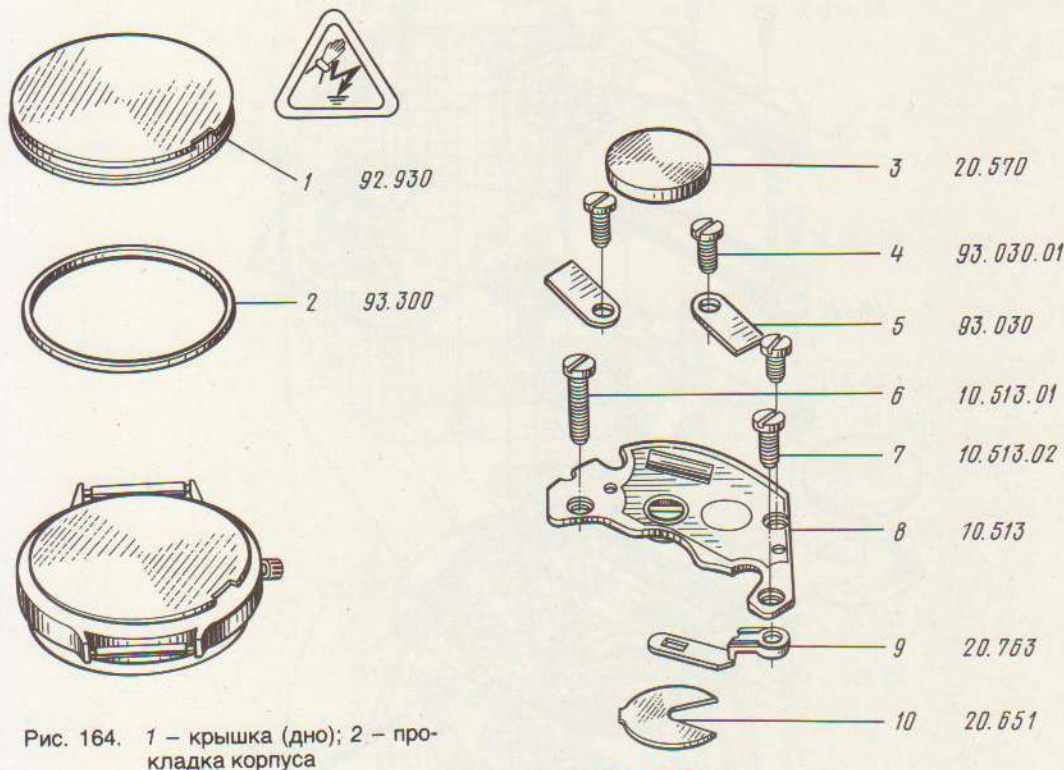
1 – крышка (дно); 2 – прокладка корпуса
